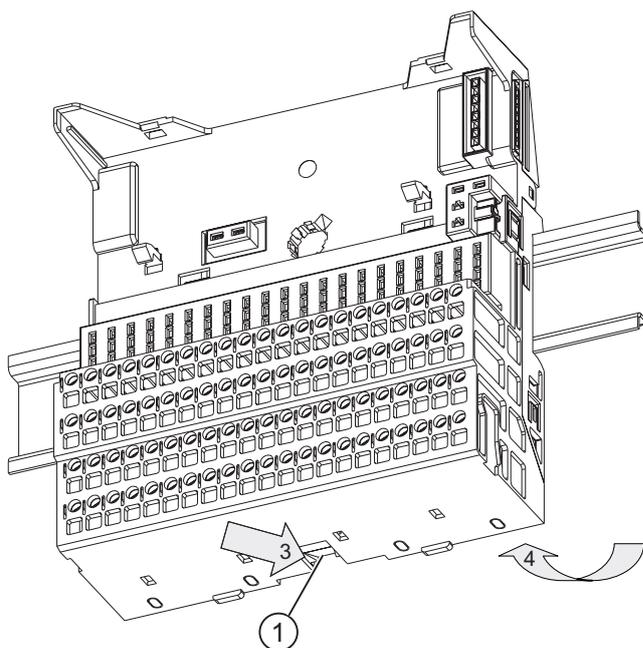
Desmontar un módulo de terminales para módulos COMPACT
